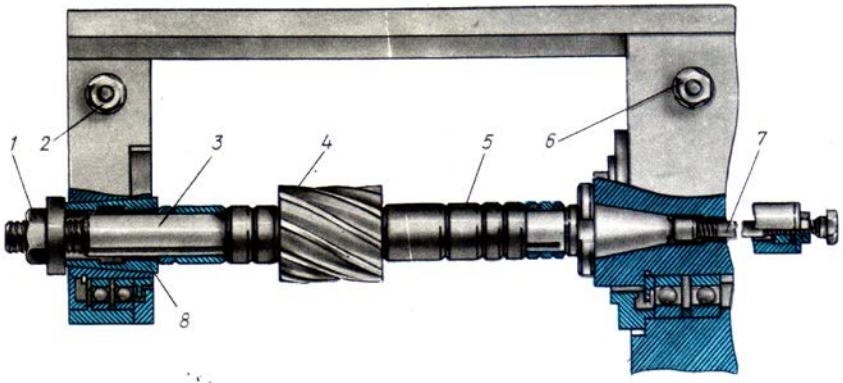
Схема установки цилиндрической фрезы на горизонтально-фрезерном станке: 1, 2, 6 – гайки; 3 – оправка; 4 – фреза; 5 – кольца; 7 – шомпол
